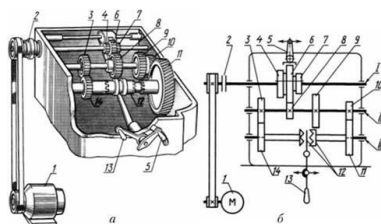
Коробка скоростей токарного станка (а), его кинематическая схема (б).
